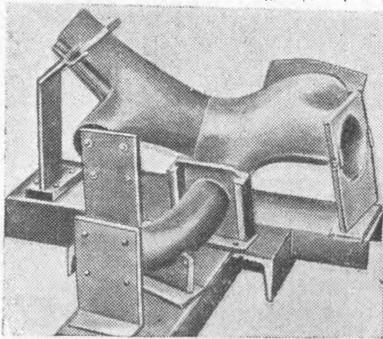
Приспособление для сборки и прихватки промежуточной секции коллектора.
